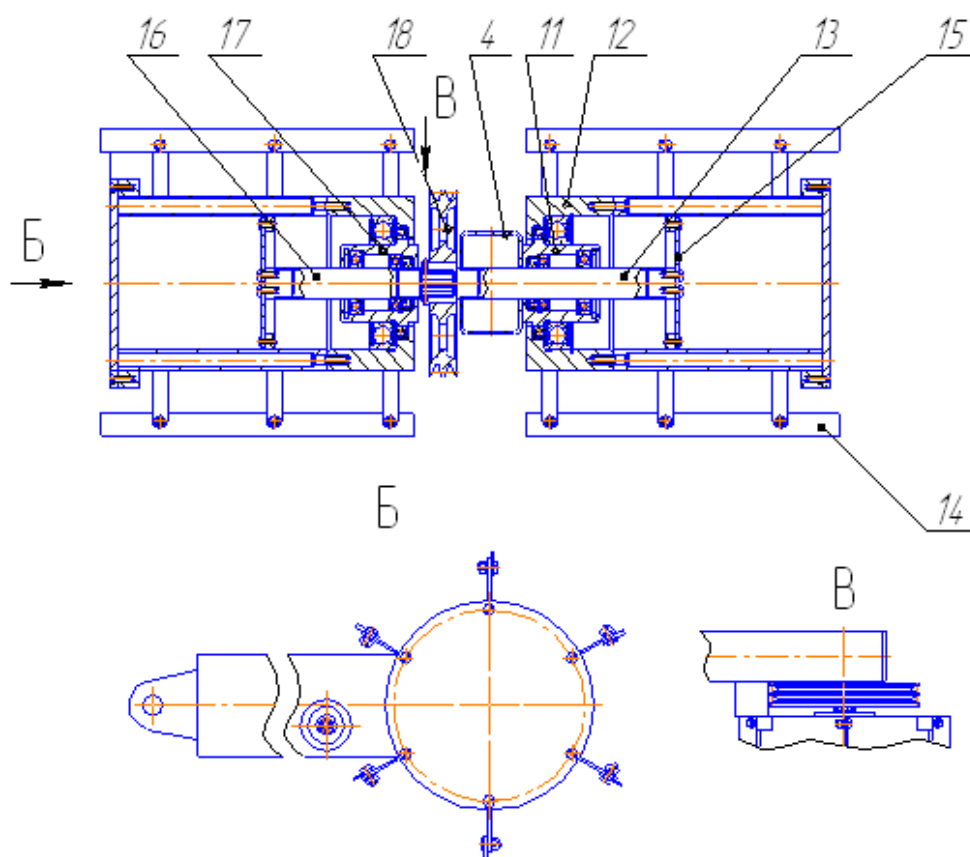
Барабан очищающий 4 – стрела; 11 – опора неподвижная; 12 – корпус; 13 – вал; 14 – щетка; 15 – крышка; 16 – вал; 17 – опора; 18 – шкив;
